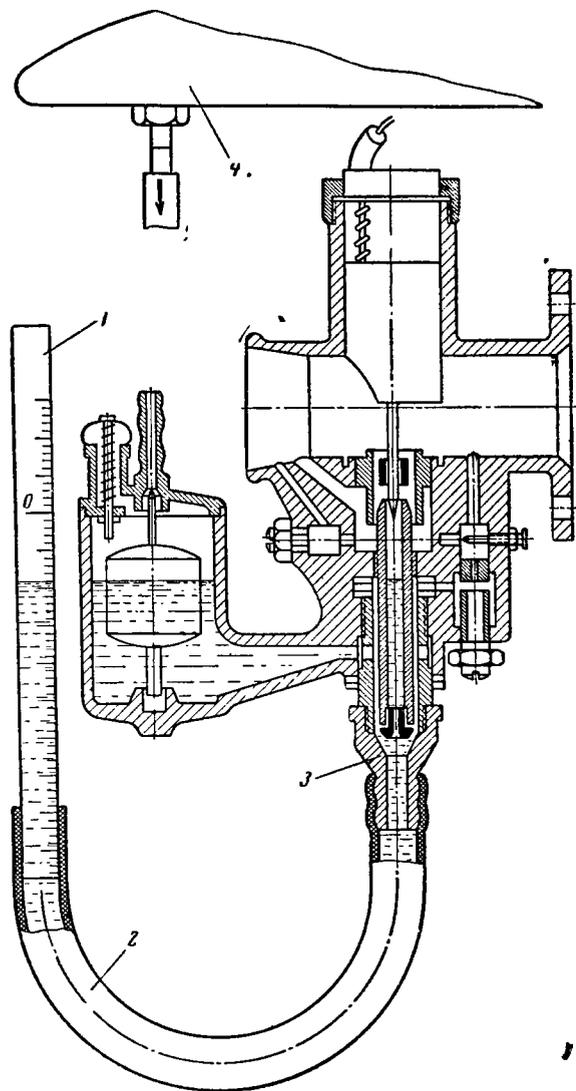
Проверка уровня топлива в поплавковой камере карбюратора: 1—стеклянная трубка с внутренним диаметром не менее 8 мм; 2—резинная трубка; 3—специальный штуцер; 4—топливный бак.
